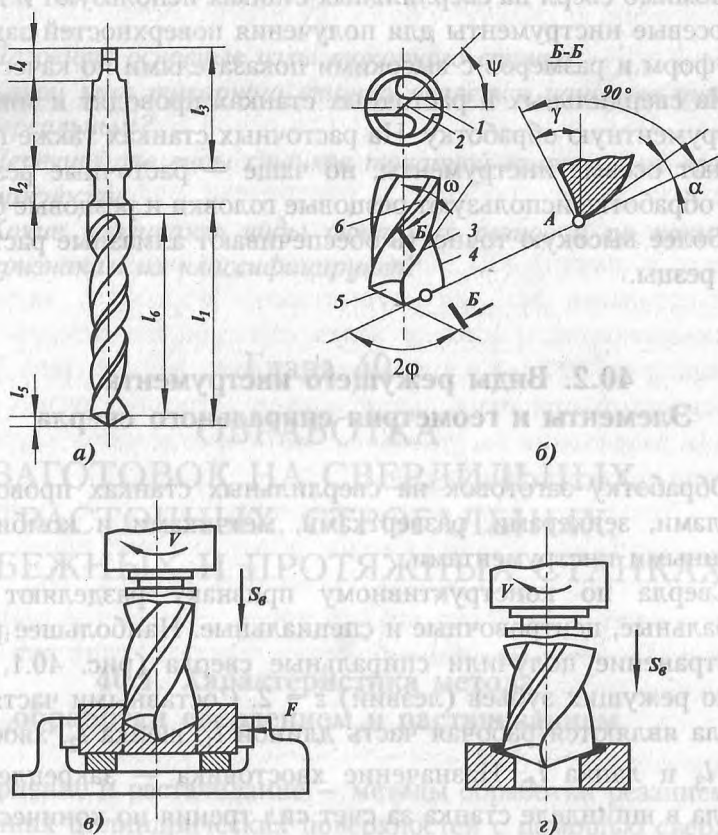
Спиральное сверло: а — общий вид; б — геометрические параметры сверла; в — сквозное сверление; з — рассверливание
